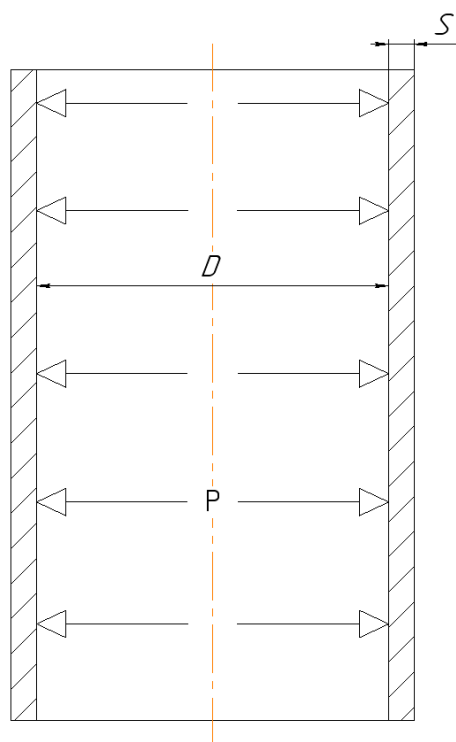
Розрахункова схема циліндричної обичайки.
